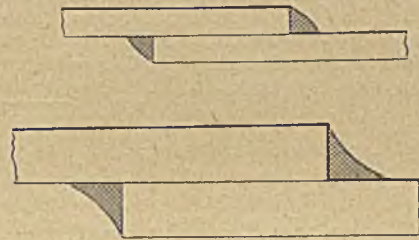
Gewölbte und hohle Schweißung.
